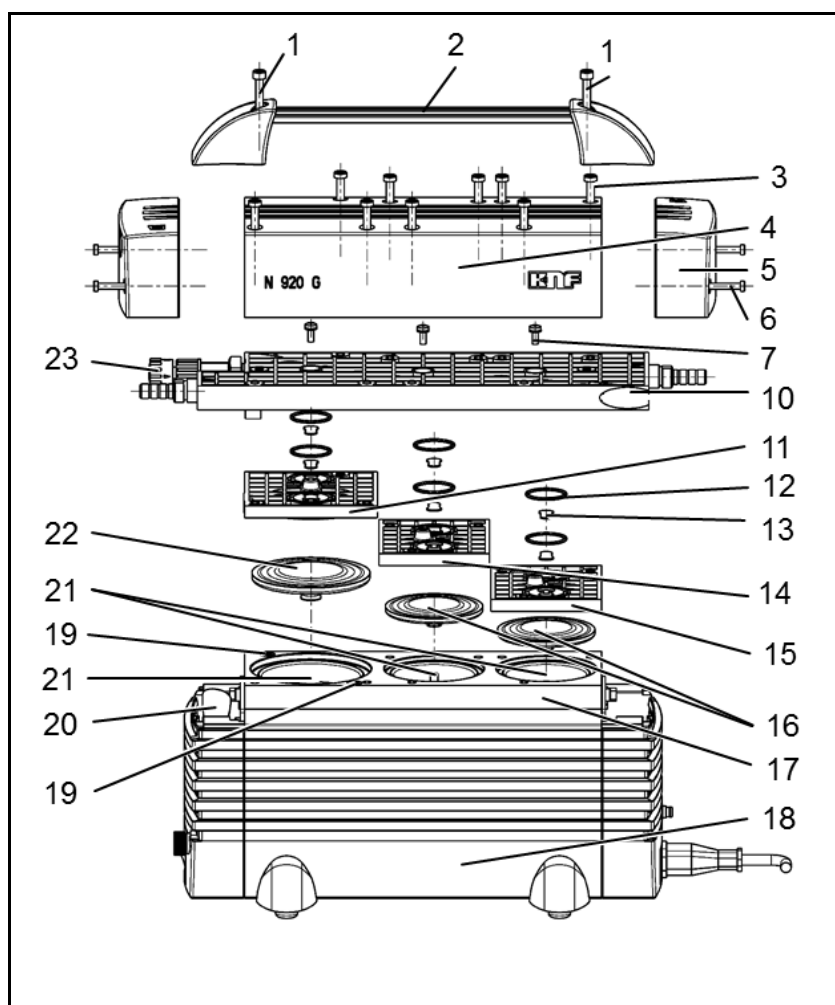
Explosionszeichnung N 920 KT.29.18G
